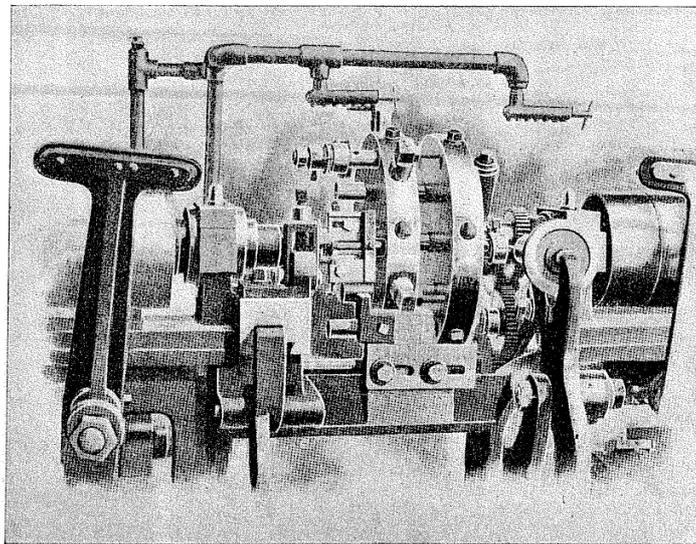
Machine à vis *Spencer*, détail du double revolver
